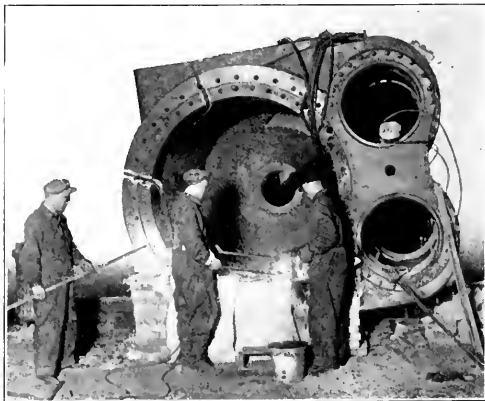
SOLDANDO EL CILINDRO DE BAJA PRESIÓN.
